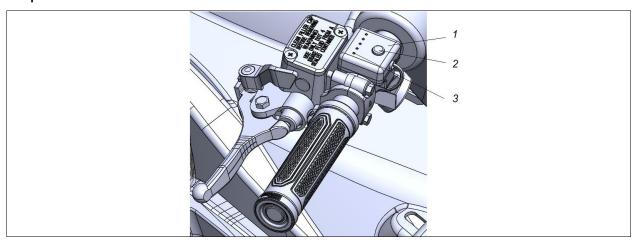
Выключатель нагревателей рукояток руля и рычаг газа.
